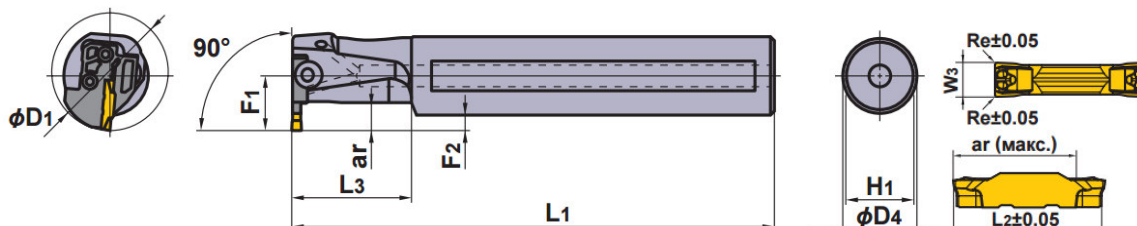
Канавочный резец с державкой GYDR32S90C-M20L и пластиной GY2G0500H080N-MF
